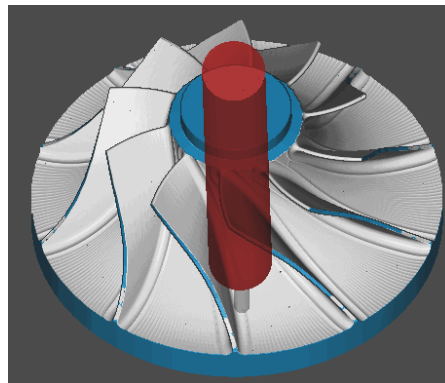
Blade finishing process strategy (rear view) of 27mm diameter impeller
